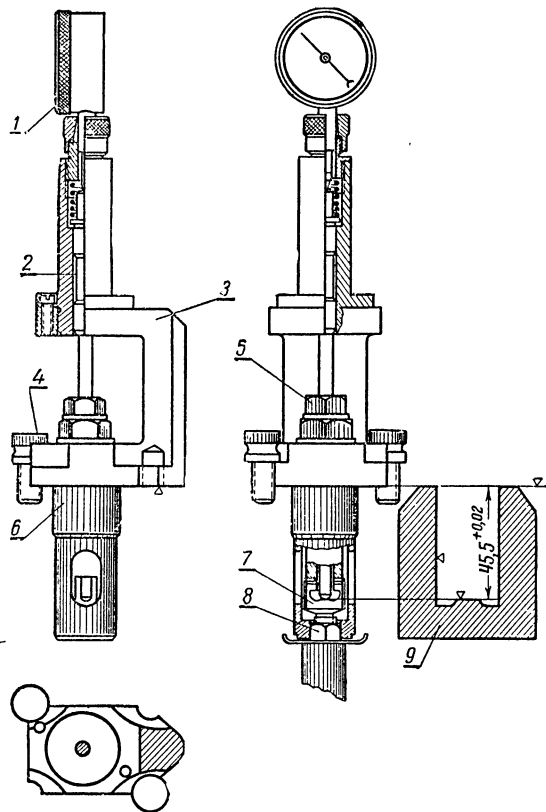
Приспособление для регулировки толкателей топливного насоса:
